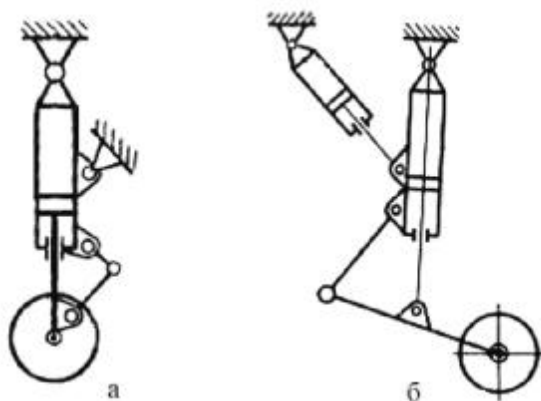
Схема балочного шасси (а) и рычажного с механизмом уборки (б).
